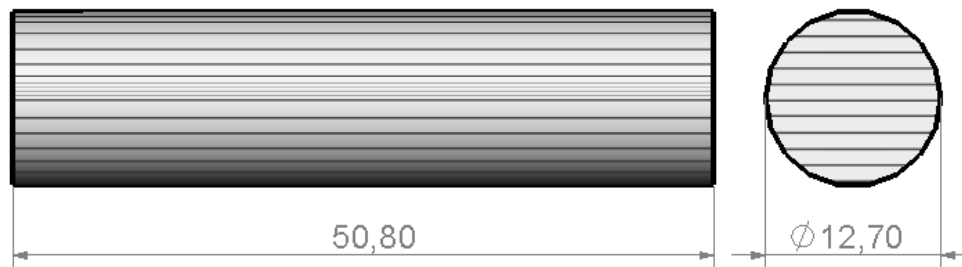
Esquema de la proveta llarga de secció circular per l'assaig a compressió (mesures en mm)
